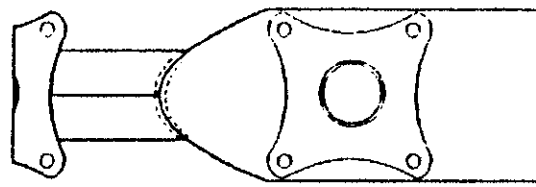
Контроль сварного шва накладок нижнего пояса продольной балки рамы
